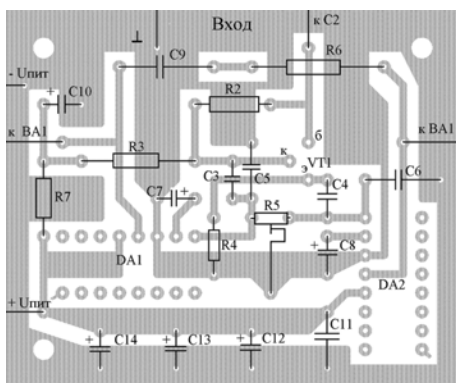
Эскиз монтажной платы одного усилителя переговорного устройства. Вид со стороны установки деталей.
